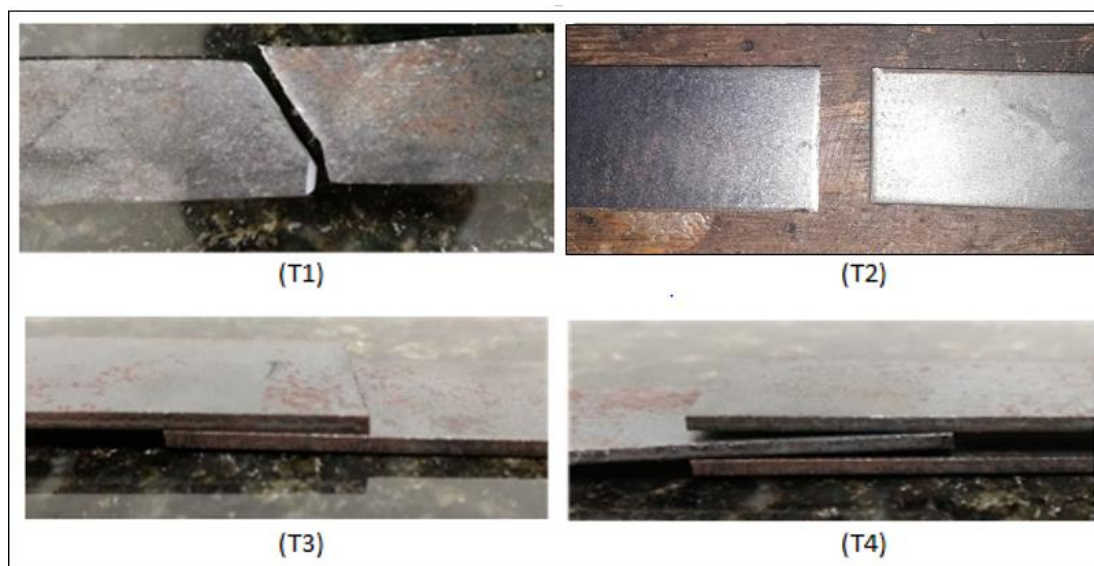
Disposição das chapas a serem soldadas.
